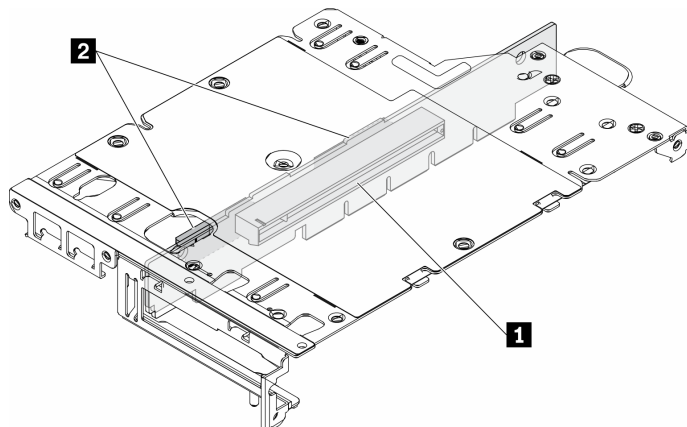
Assemblage de cartes mezzanines PCIe et M.2
